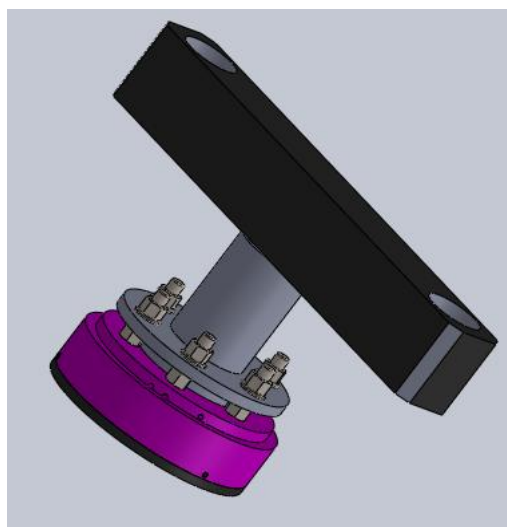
traverse-porte piston-piston plaque assemblés.
